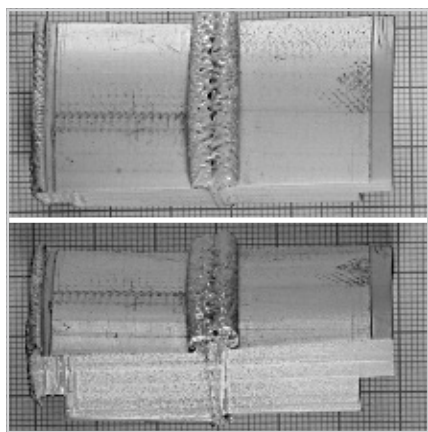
Сварной шов трубного образца из PEI, полученный при сварке нагретым инструментом встык
